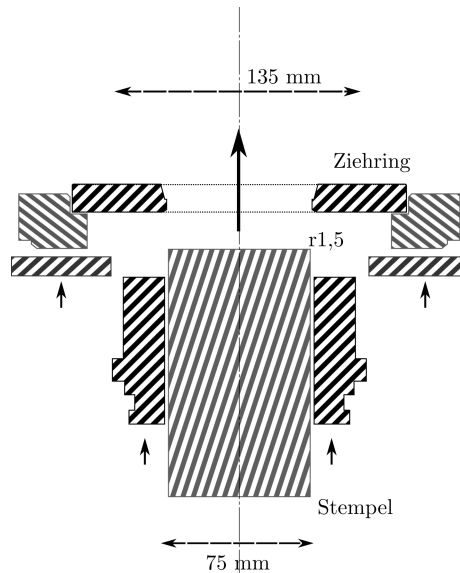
Aufbau des Napfzug Werkzeugs inklusive Schnitttring
